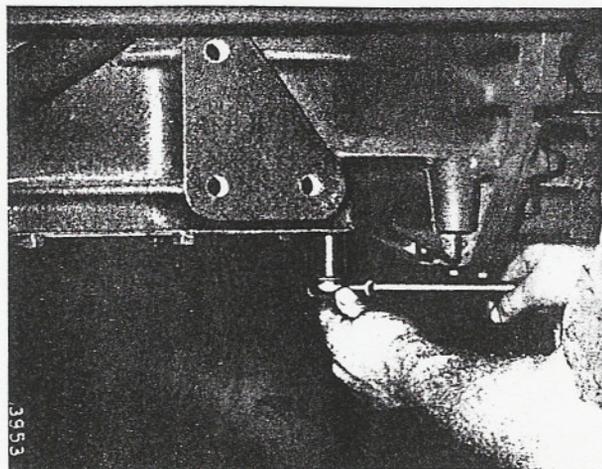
Enlèvement de la plaque de visite sous le carter d'embrayage
